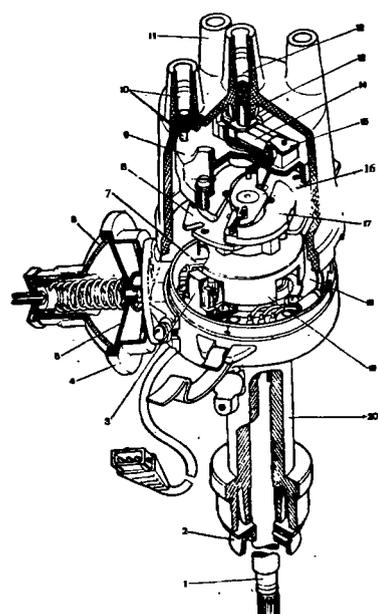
Датчик-распределитель зажигания 38.3706: 1 - валик; 2 - маслоотражательная муфта; 3 - бесконтактный датчик; 4 - корпус вакуумного регулятора; 5 - мембрана; 6 - крышка вакуумного регулятора; 7 - тяга вакуумного регулятора; 8 - опорная пластина центробежного регулятора; 9 - ротор распределителя зажигания; 10 - боковой электрод с клеммой; 11 - крышка; 12 - центральный электрод с клеммой; 13 - уголек центрального электрода; 14 - резистор; 15 - наружный контакт ротора; 16 - пластина центробежного регулятора; 17 - грузик; 18 - опорная пластина бесконтактного датчика; 19 - экран; 20 - корпус датчика распределителя зажигания
